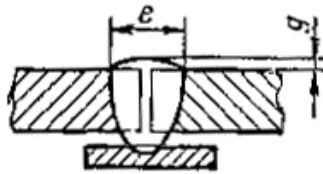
Сварное соединение С5 ГОСТ 8713-79 для сварки кольцевого шва
